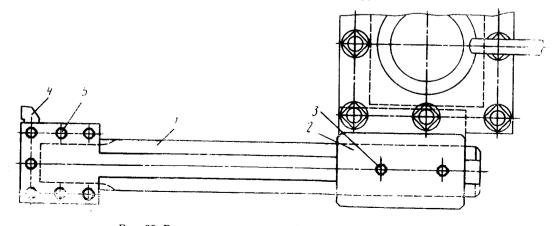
Резцовая оправка для обработки деталей над выемкой в станине
